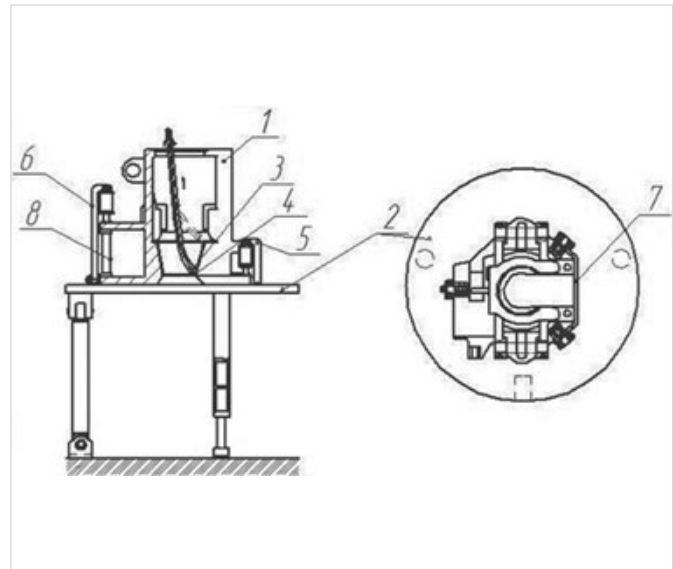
Схема установки и закрепления корпуса спайдера под наплавку. 1 — корпус спайдера, 2 — стол для наплавки, 3 — сварочная головка, 4 — наплавляемая поверхность, 5 — пневматические прижимы без откидного механизма, 6 — пневматический прижим с откидным механизмом, 7 — установочный упор, 8 — распорка
